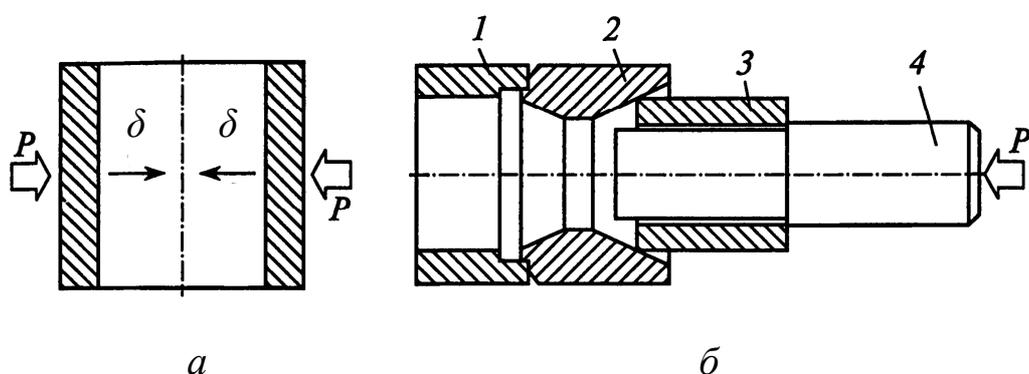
Пластическое деформирование обжатием: *a* – принципиальная схема; *б* – приспособление для обжатия втулок; 1 – опорная втулка; 2 – матрица; 3 – восстанавливаемая втулка; 4 – оправка
